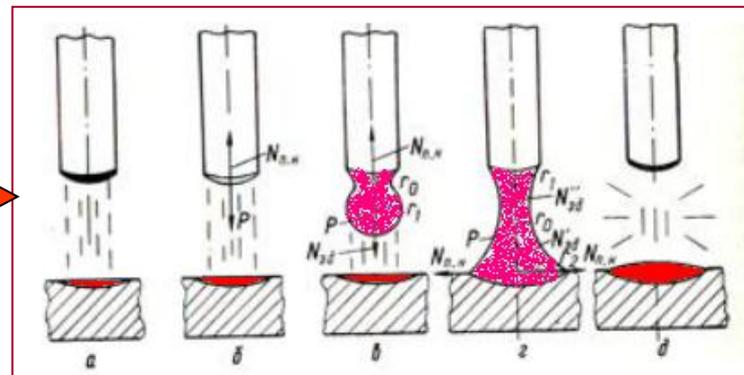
Схема образования капли и переноса ее в сварочную ванну.
